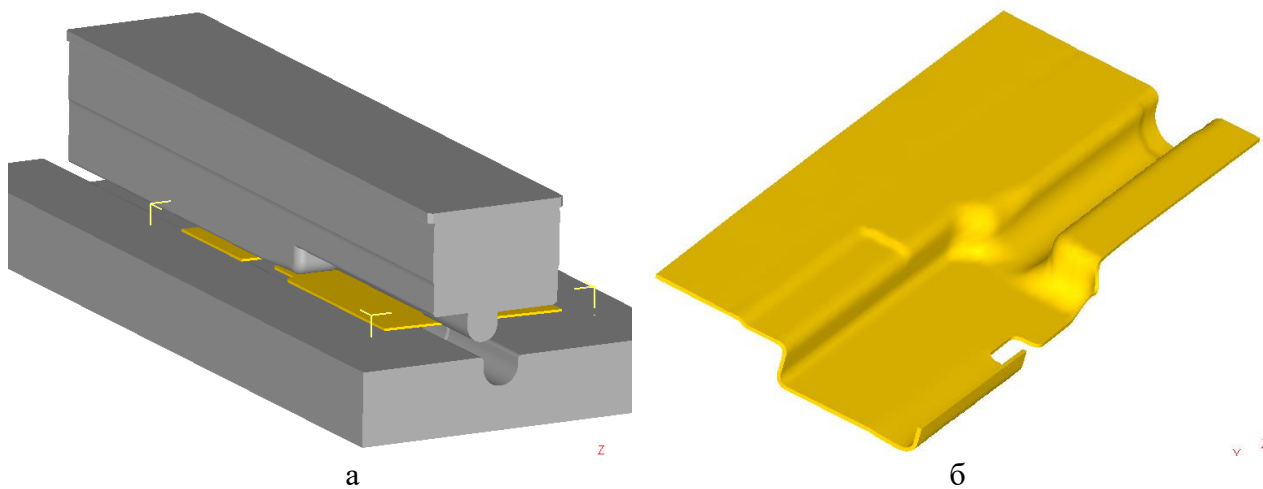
Моделювання деформування заготовки з початковою геометрією:
